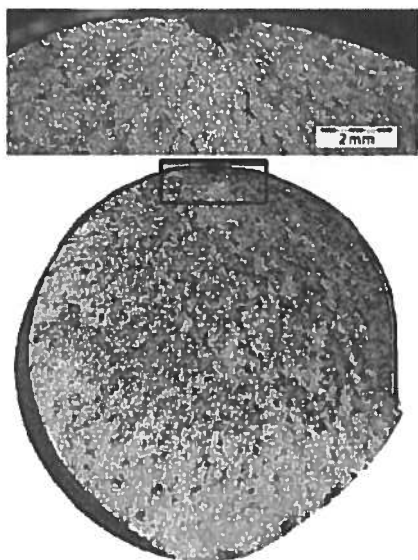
Superfície de fratura e pormenor no local de iniciação da fissuração.
